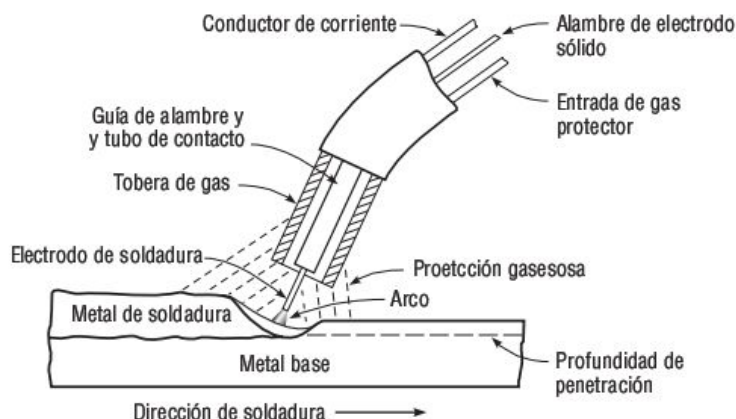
Esquemático de la soldadura a gas.
